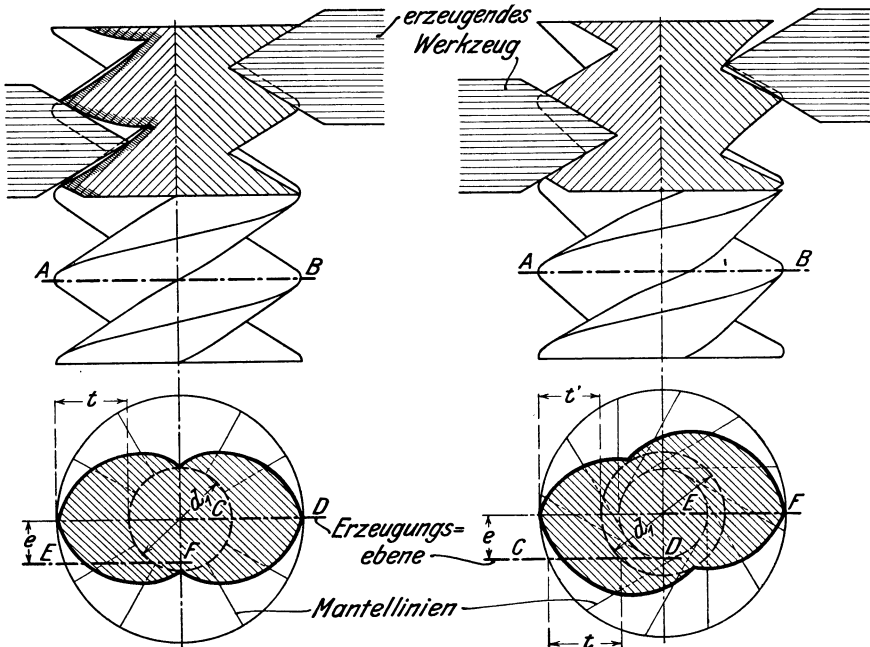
Verfälschung der Gewindeform durch falsche Einstellung des erzeugenden Gewindestahles.
